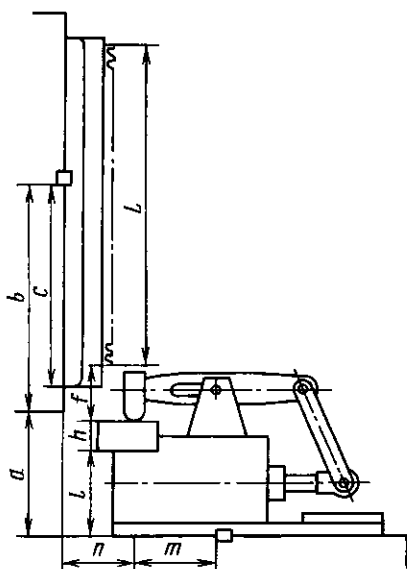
Схема наладки вертикально-протяжного станка для наружного протягивания
